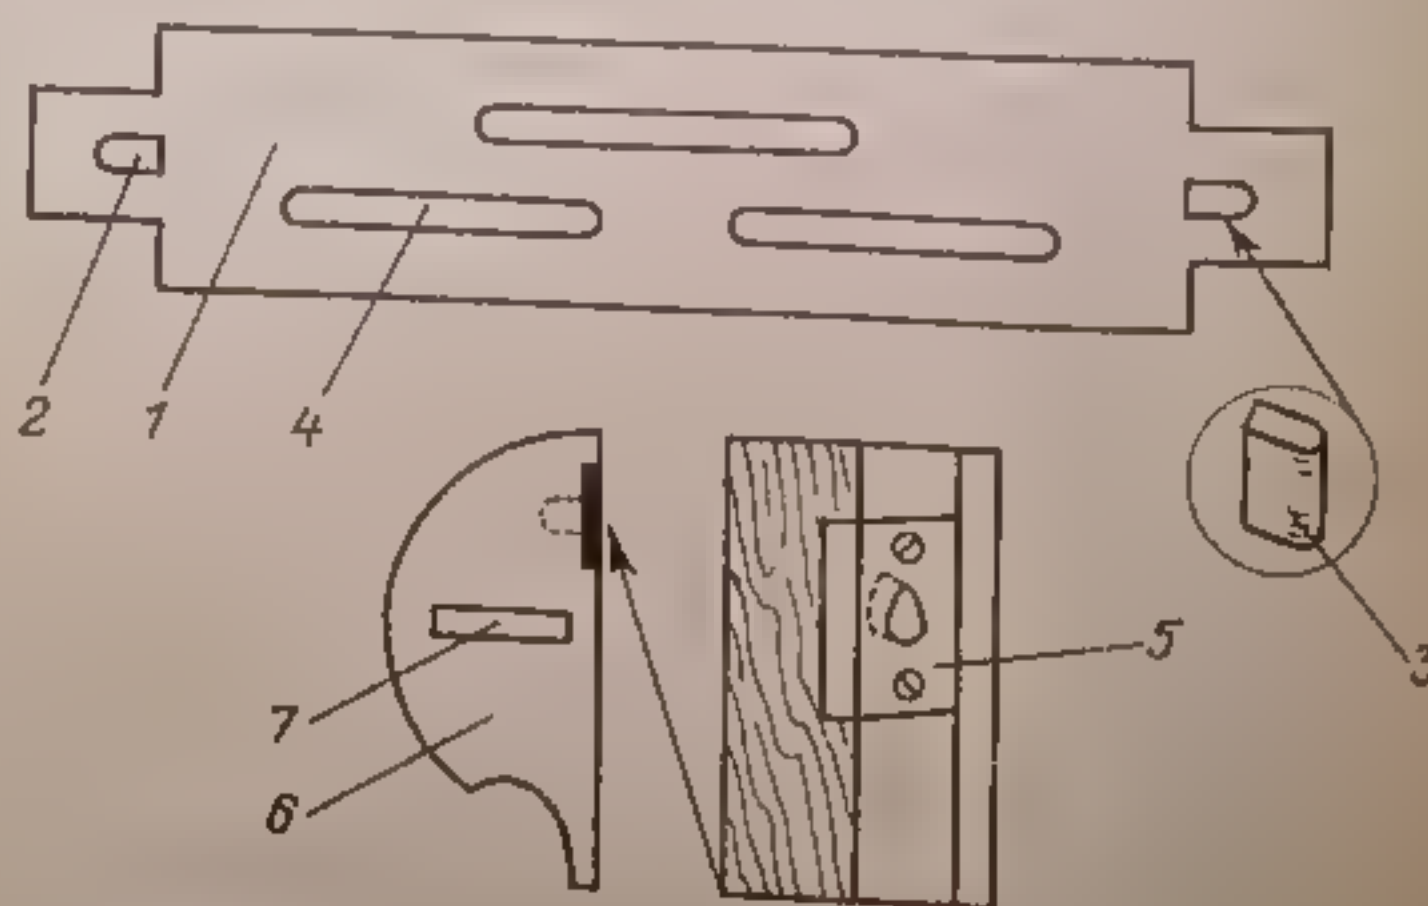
Детали кухонной полки: 1 — полка; 2 — отверстие для клина; 3 — клин; 4 — пропил для крышки; 5 — узел крепления полки; 6 — боковина; 7 — пропил для проушины полки
